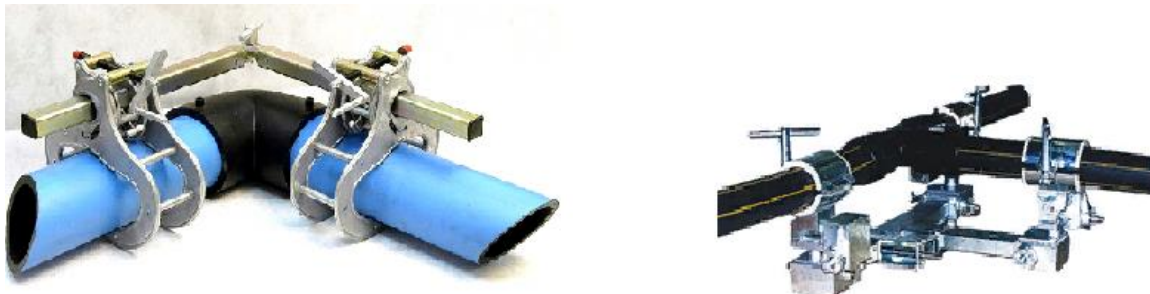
Позиционеры для сварки деталей муфтового типа и седловых отводов
